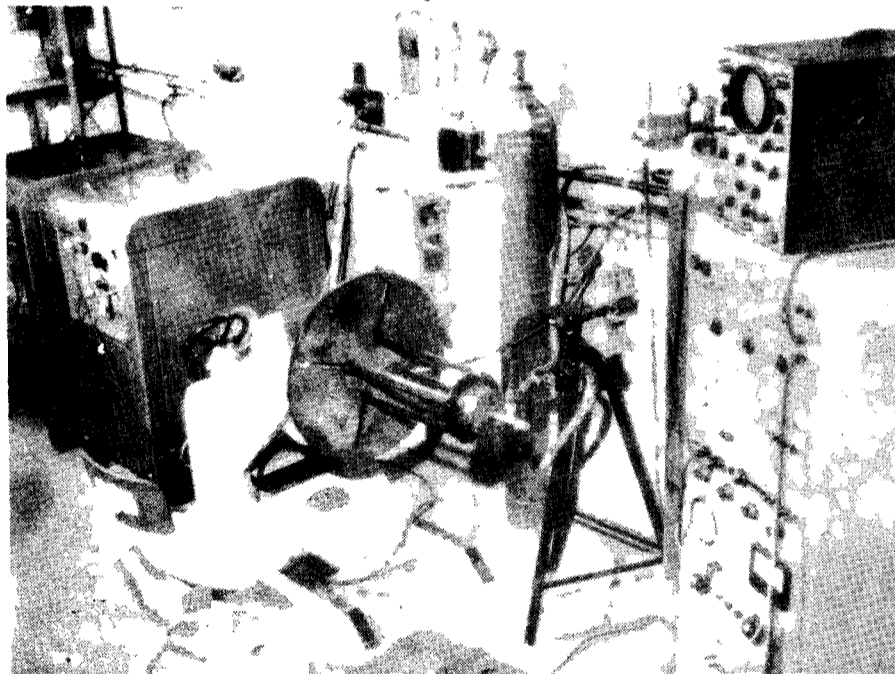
Aspecto general del equipo de soldadura.
